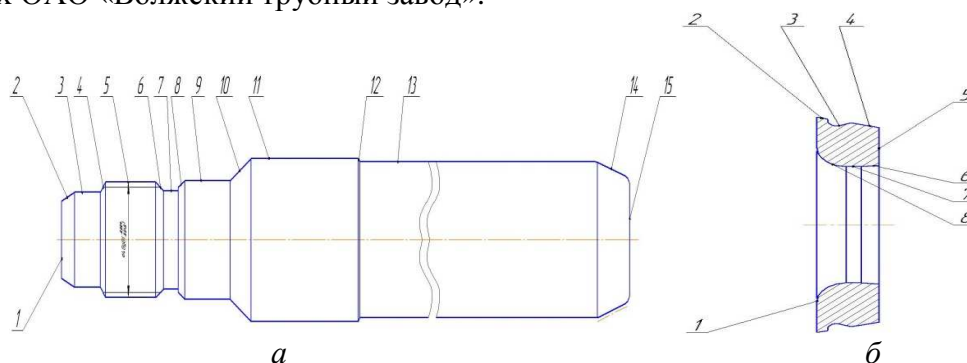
Калибрующие детали – игла (а), матрица (б)
